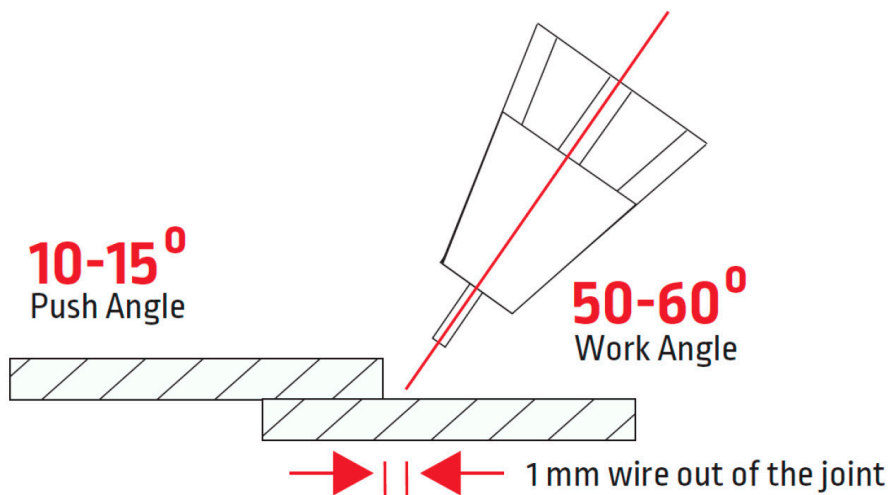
Accesorio de soldadura y configuración de juntas para todos los estudios de ingeniería de soldadura.
